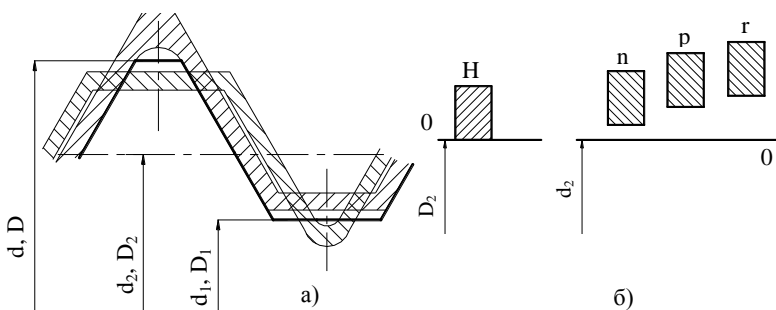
Посадка з натягом метричної різьби: а) схема полів допусків; б) основні відхилення
